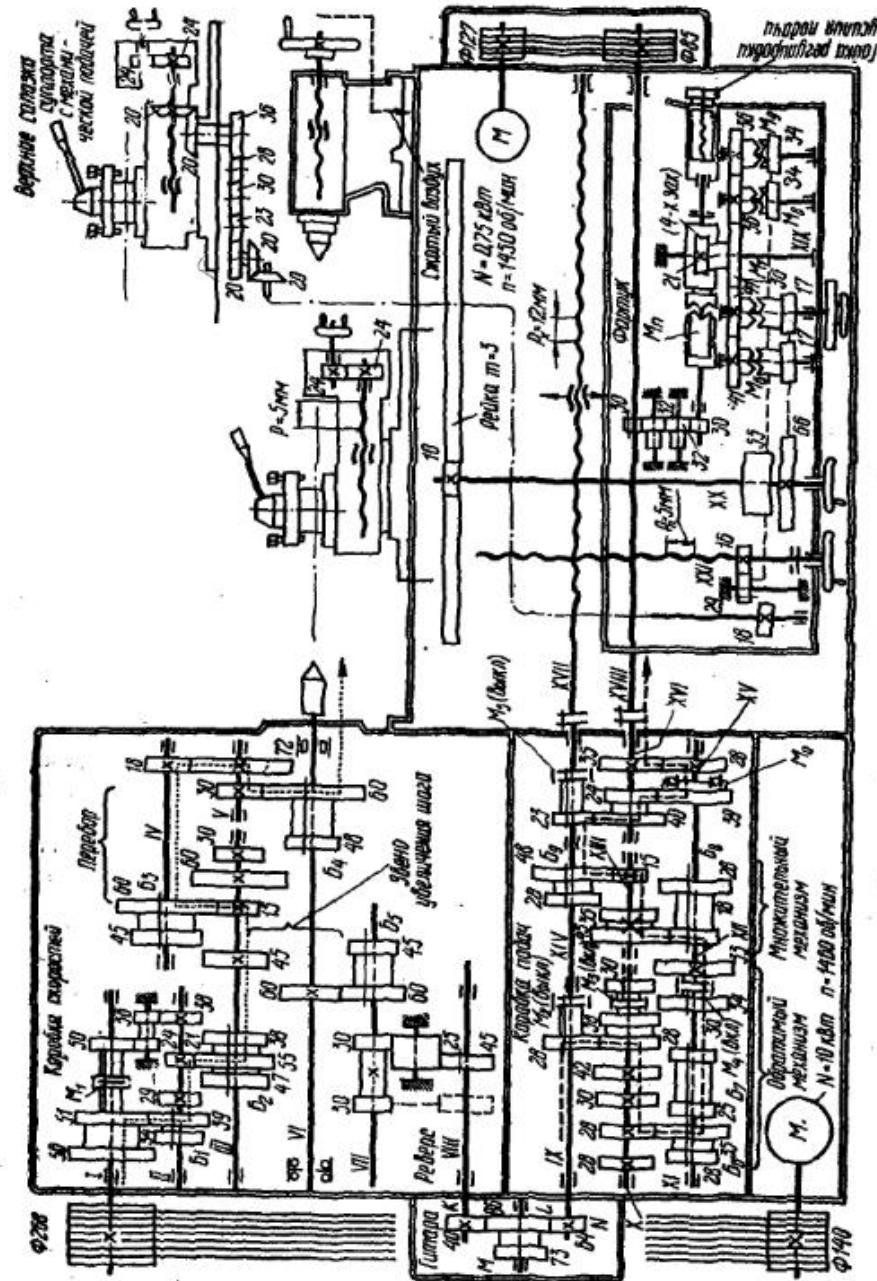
Кинематическая схема привода главного движения станка 16К20
